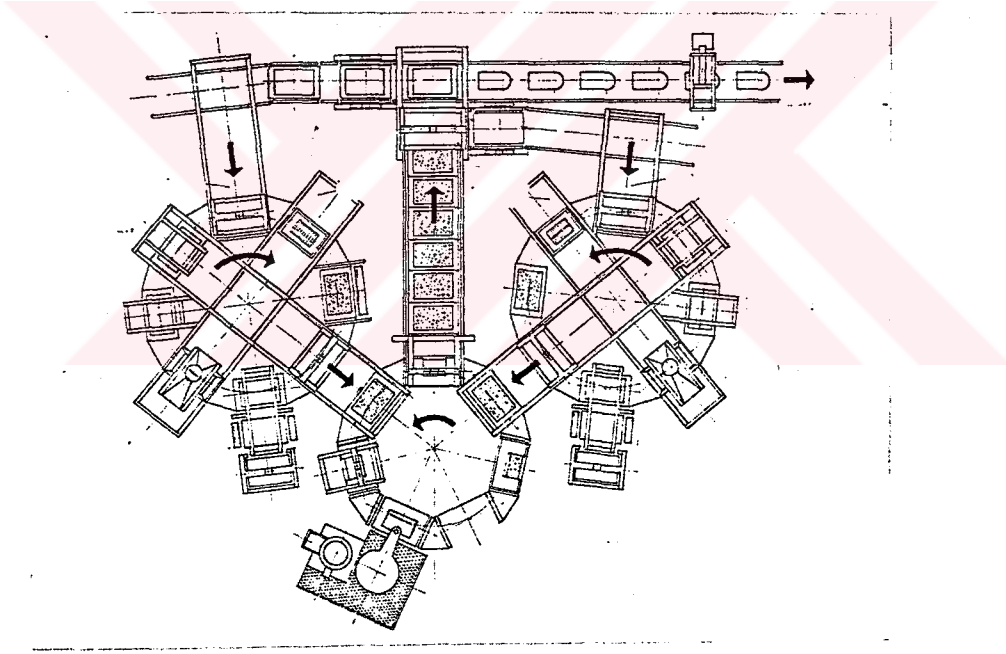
Vakum Döner Kalıplama Tesisi /1/.
